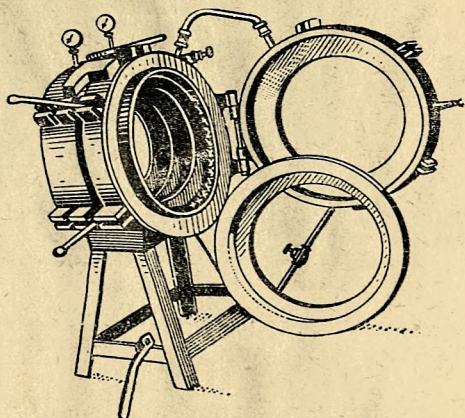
Двойной индивидуальный вулканизатор со сменными вкладышами
